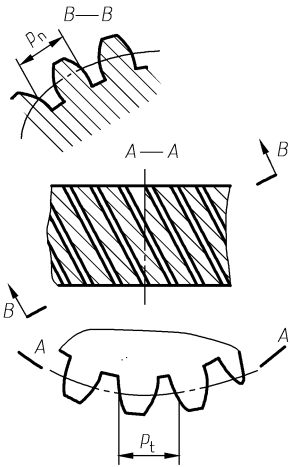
斜齿圆柱齿轮法向齿距和端面齿距
